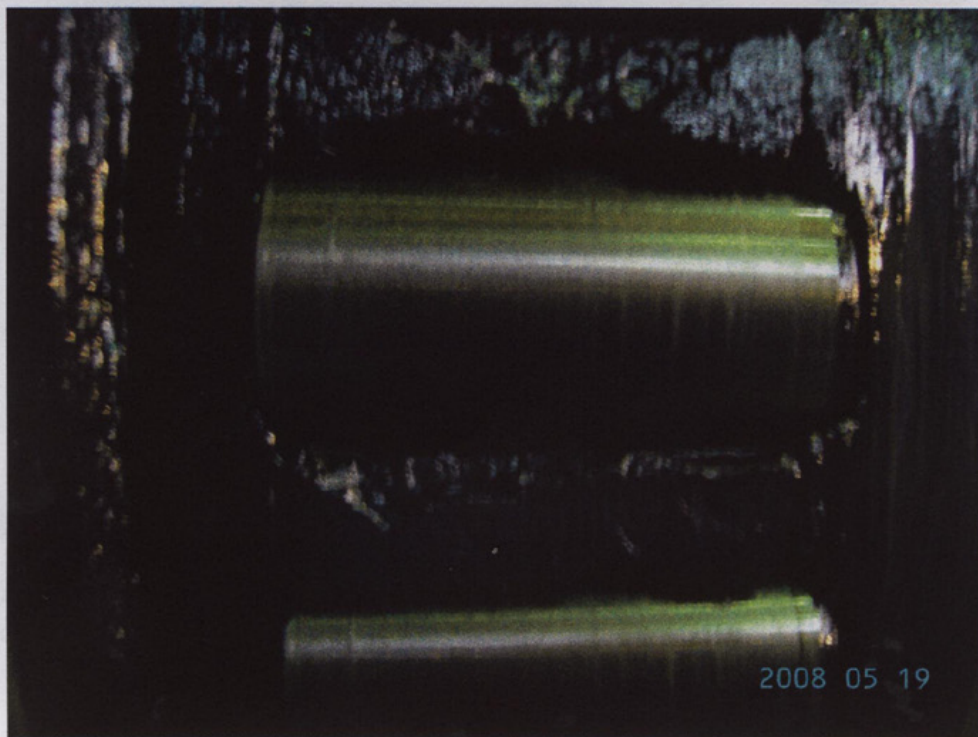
Ролики внутреннего подшипника после работы на смазке МС-1000.
